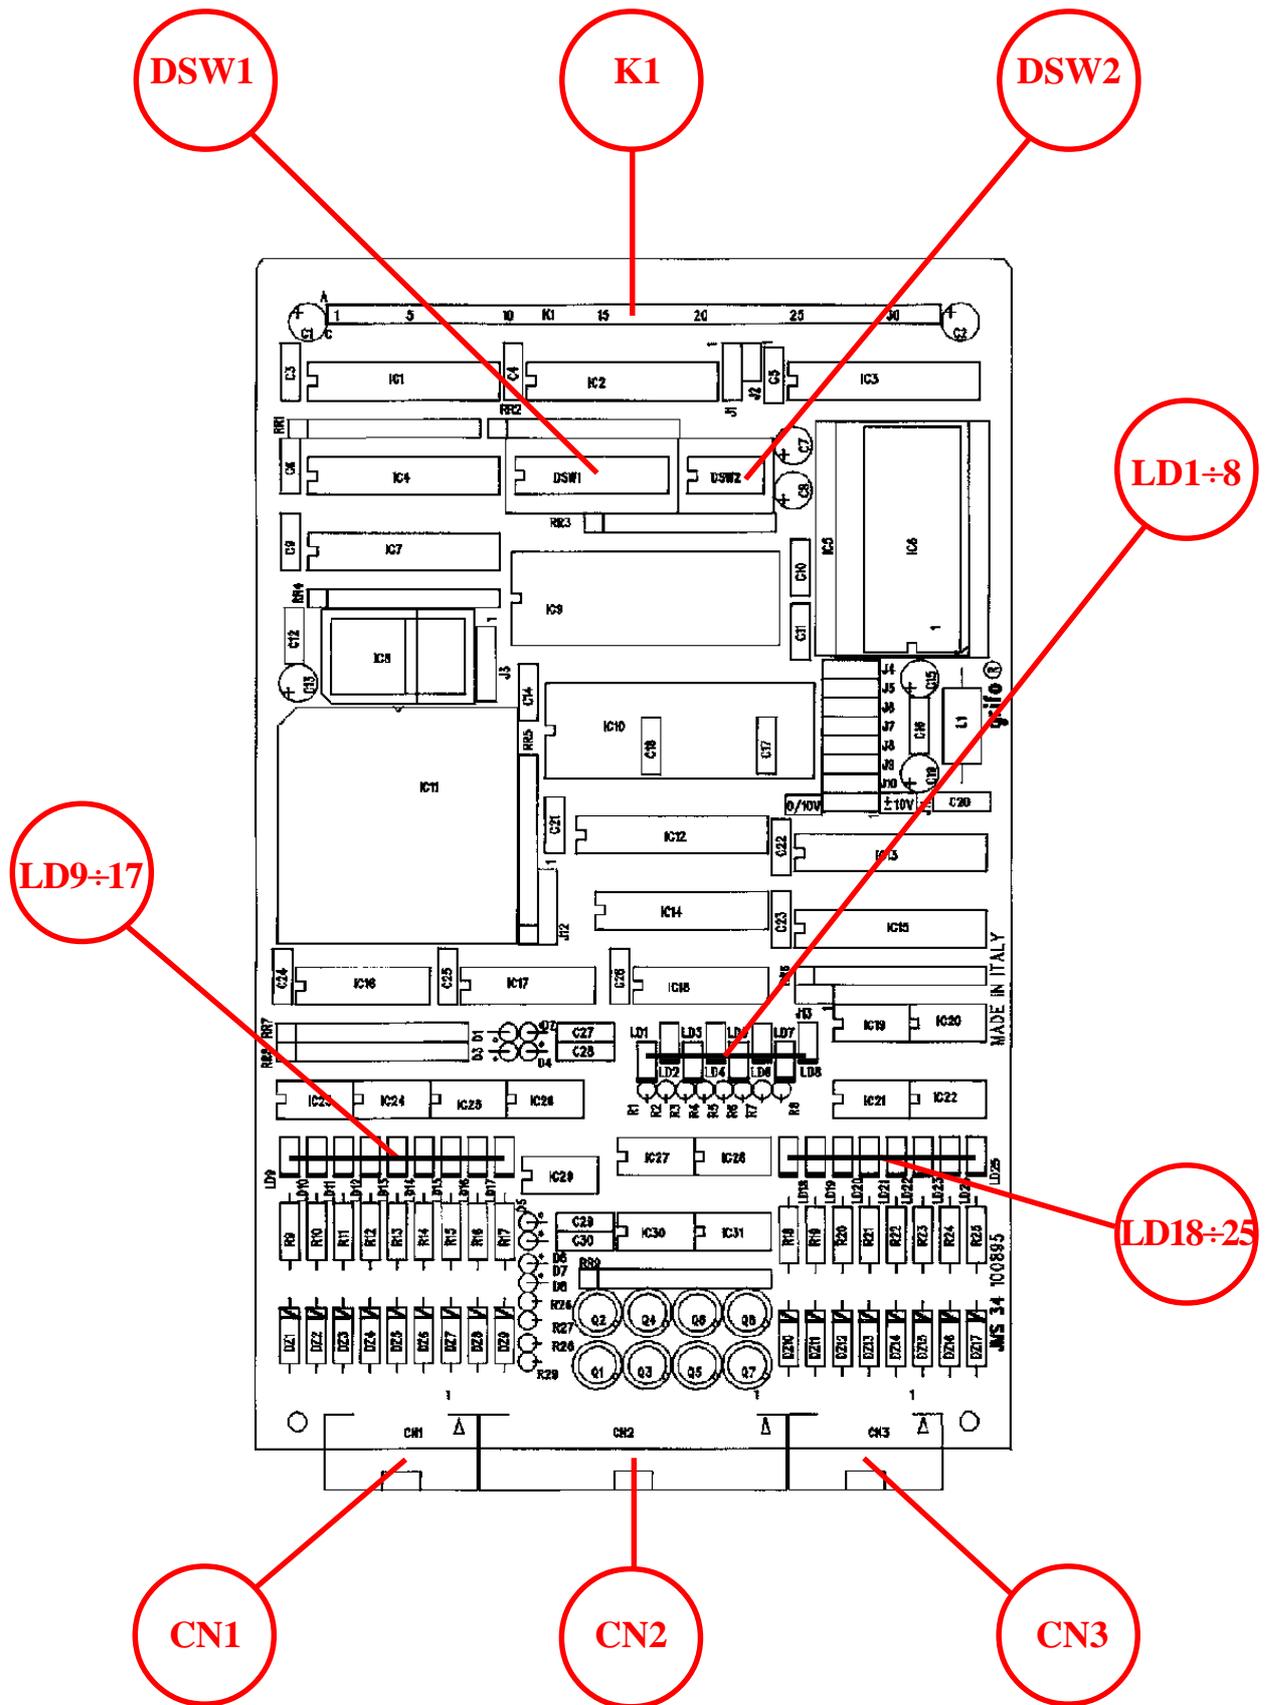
DISPOSIZIONE DI CONNETTORI, LEDS E DIP-SWITCH
